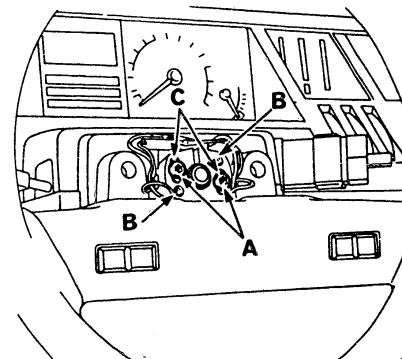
Die Schrauben A müssen in den Bohrungen B eingesetzt werden, um das Lenkrad abzudrücken. In den Langlöchern C lässt sich das Lenkrad einmitten.
